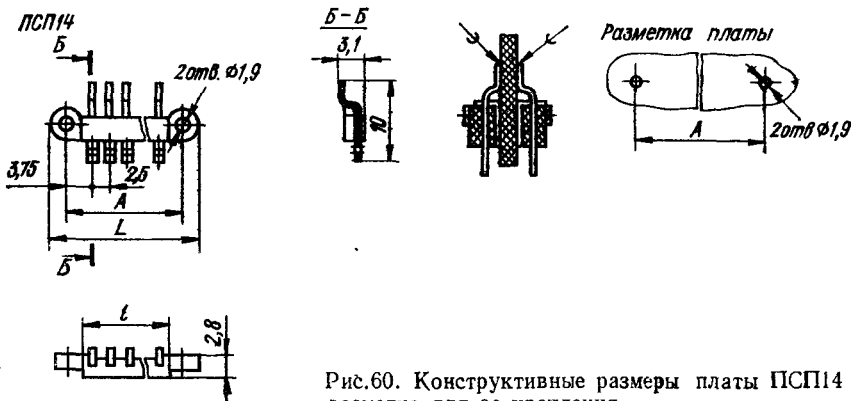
Конструктивные размеры платы ПСП14 и разметка для ее крепления
